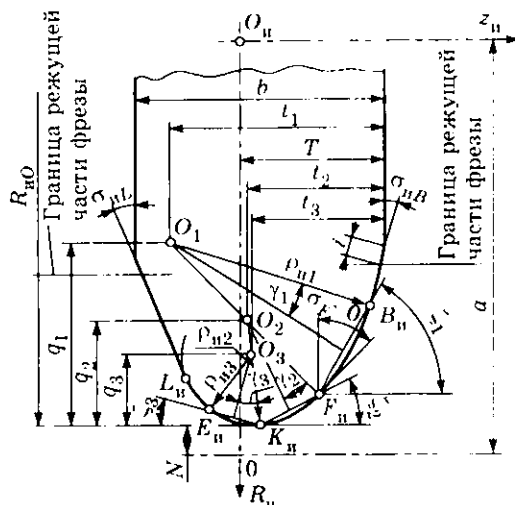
Схема замены точного профиля дисковой фасонной фрезы для обработки канавки сверла дугами окружностей
